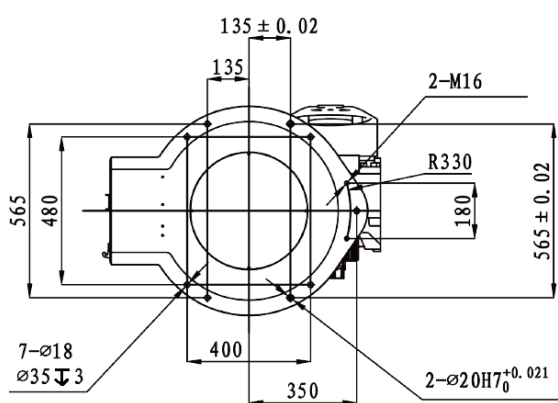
Габаритные чертежи робота-манипулятора SR20-1700.
